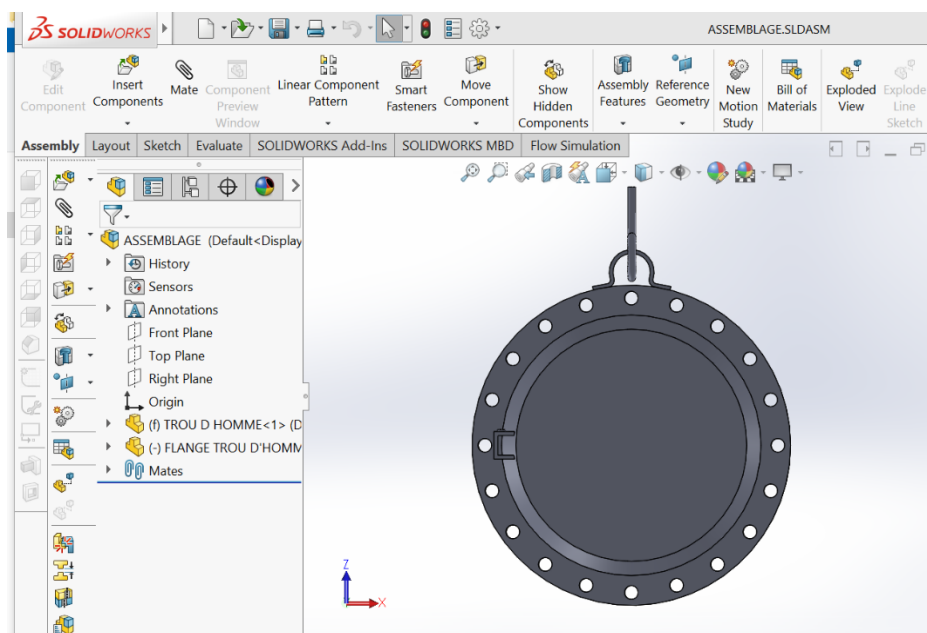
BRIDE PLEINE 24" ASSEMBLE EN SOLIDWORKS VUE DE FACE
